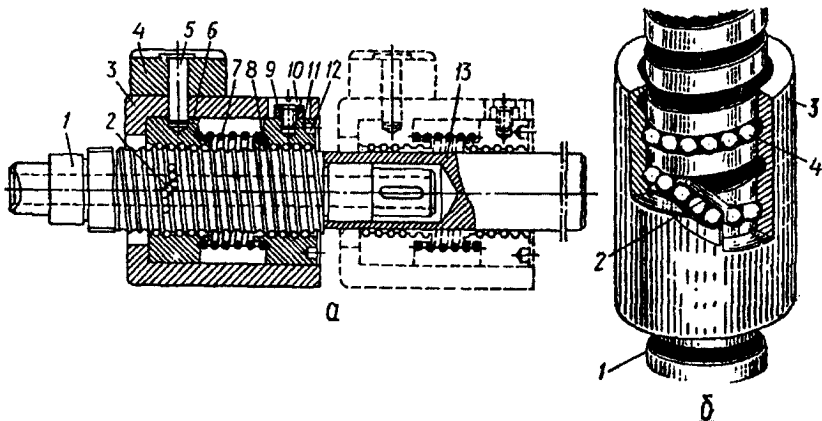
Схема (а) і конструкція (б) передачі “гвинт-гайка кочення”
